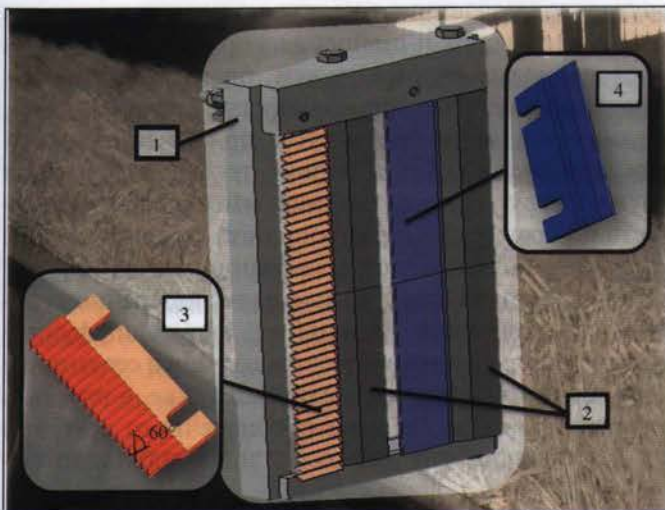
Новая компоновка двухрядной ножевой рамы: 1 — двухрядная ножевая рама; 2 — поворотные стойки рамы; 3 — кенигсфельдский нож; 4 — плоский нож
